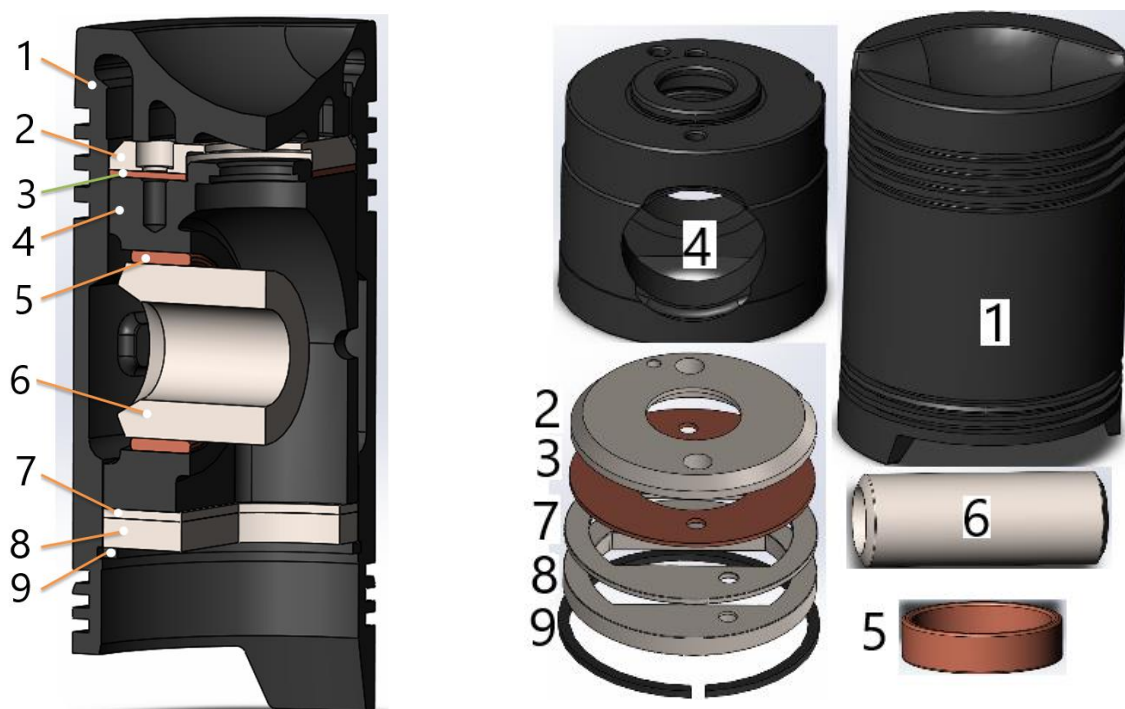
Конструкція поршня 10Д100: 1 – стакан поршня; 2 – плита верхня; 3 – прокладка верхня; 4 – вставка; 5 – втулка бронзова; 6 – палець; 7 – прокладка нижня; 8 – плита нижня; 9 – кільце стопорне
